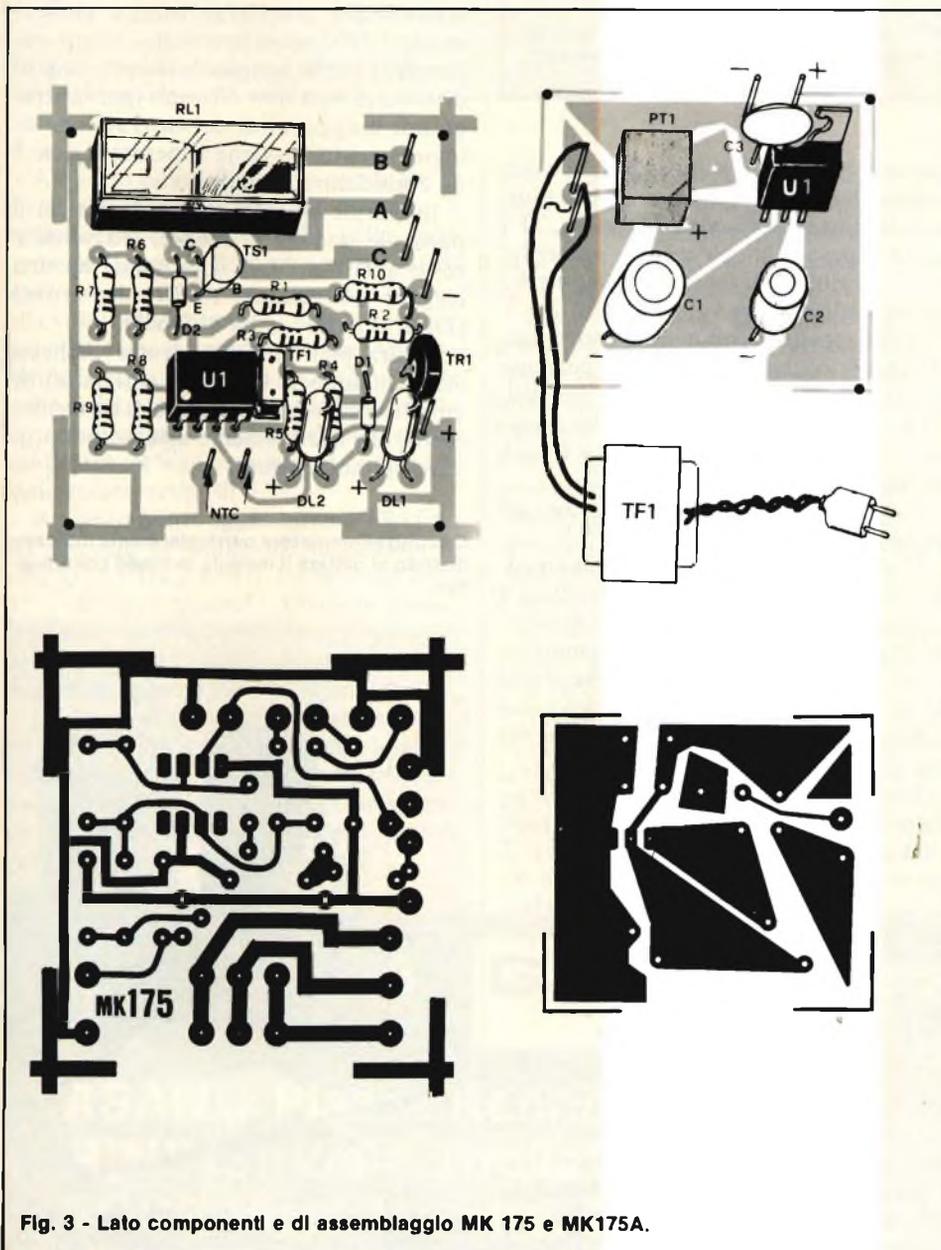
Lato componenti e di assemblaggio MK 175 e MK175A.
